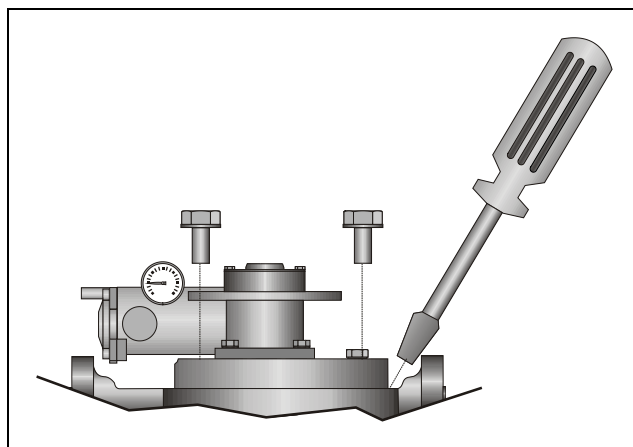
Desserrer les vis hexagonales sur le couvercle du filtre
